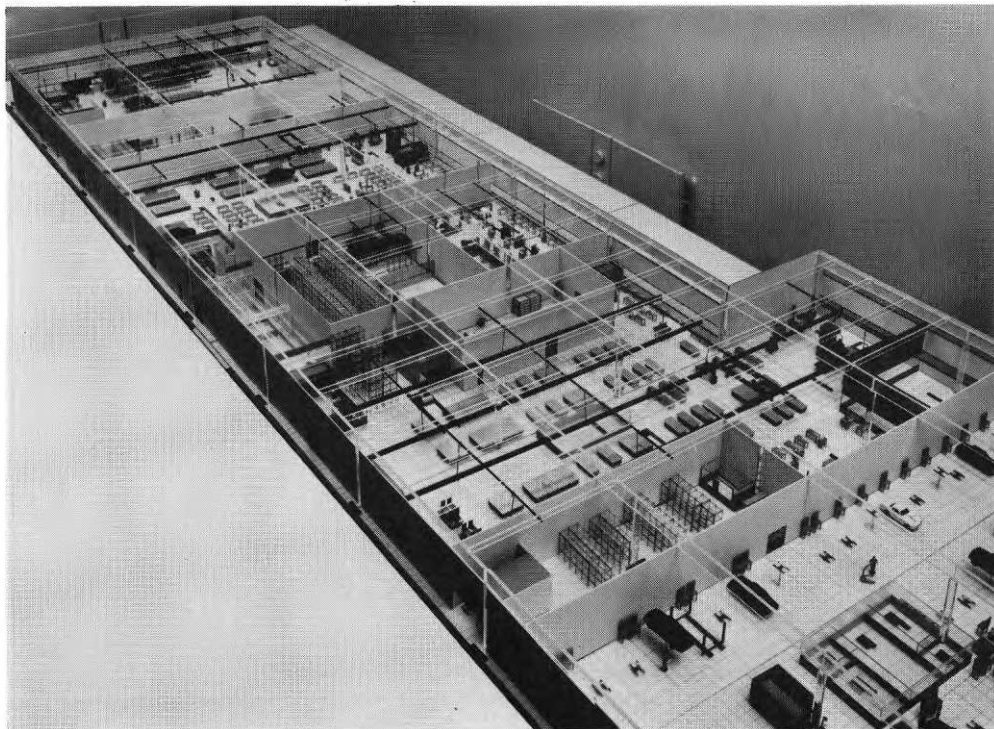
Layoutmodell, verkstadsindustrimodell,
